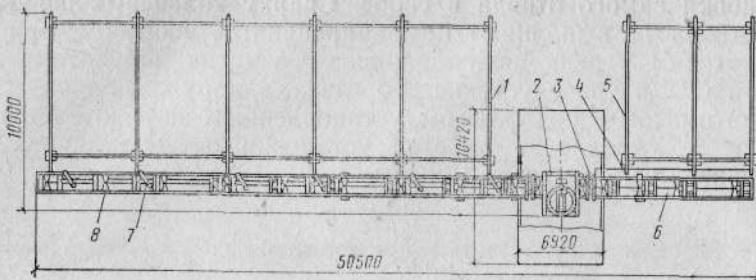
Схема стационарной установки РУСТ-630 для сборки и сварки секций трубопроводов с  $D_y=80\ldots600$  мм
